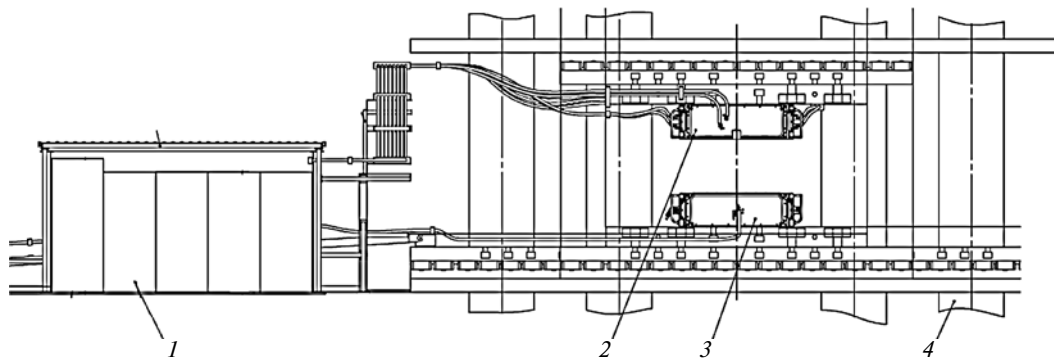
Система индукционного нагрева штамповой оснастки с плоскими индукторами:
